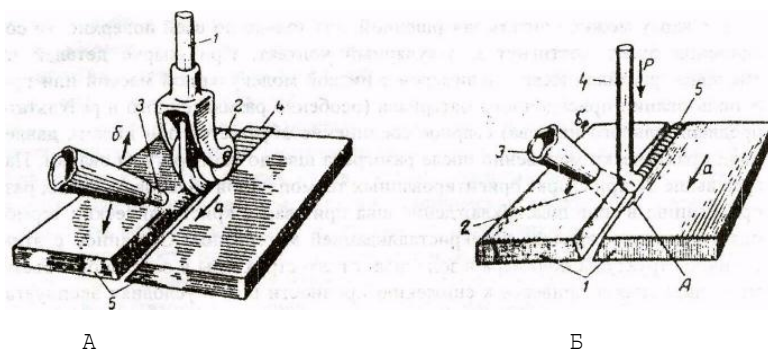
Схема сварки нагретым газом: А) с прокаткой присадочного прутка роликом : 1- присадочный пруток; 2-прижимной ролик; 3-сопло; 4 - сварной шов; 5- соединяемые детали, *а*-направление сварки , *б* - направление манипулирования сварочной горелки; Б) с применением присадочного материала: 1- свариваемые детали; 2- струя нагретого газа; 3- - наконечник нагревателя; 4 -присадочный пруток; 5 - сварной шов; *а* - направление сварки.
